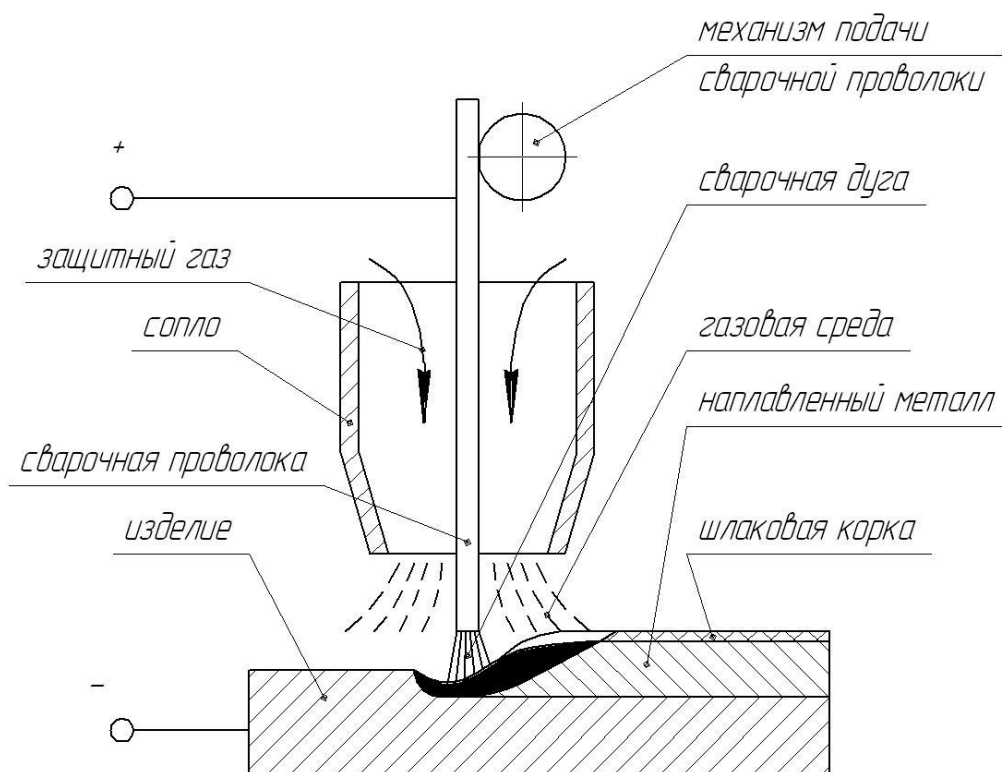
Схема механизированной сварки с применением плавящегося электрода в среде инертного газа
